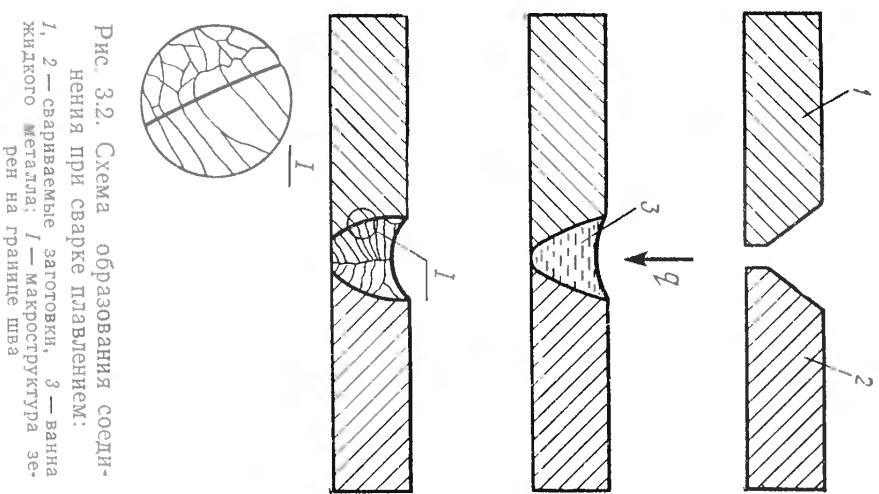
Схема образования соединения при сварке плавлением:
